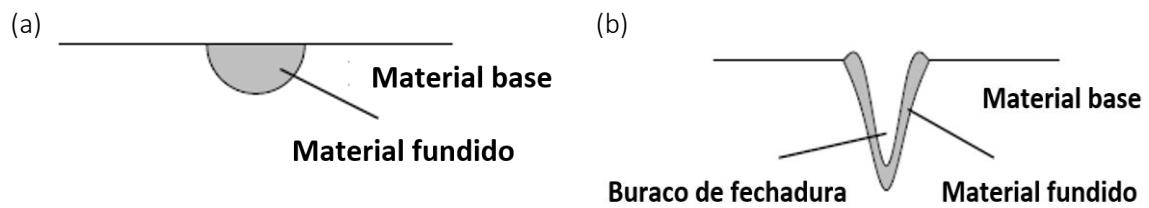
Esquema da junta de soldadura originada pela LBW. (a) Soldadura por condução, (b) soldadura por penetração [47].
